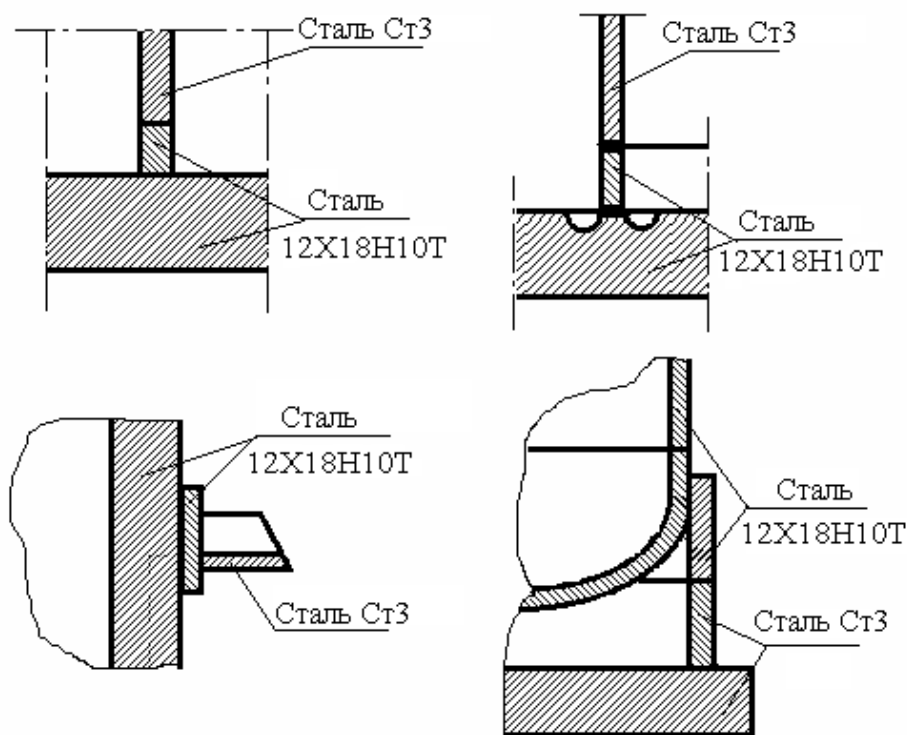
Способы сварки легированной и углеродистой стали
